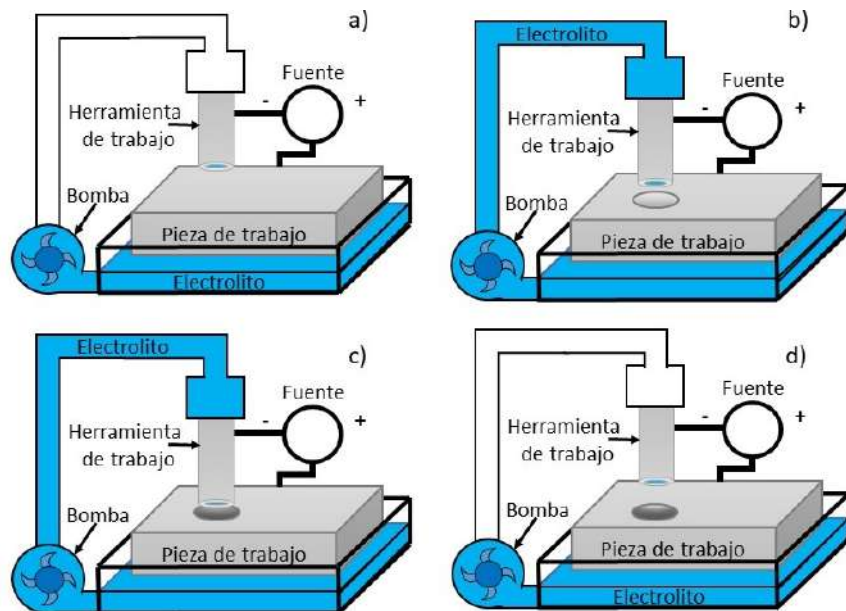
a) Herramienta y pieza de trabajo antes del maquinado. b) Herramienta de trabajo realizando el maquinado sobre la pieza de trabajo. c) Herramienta de trabajo deja de maquinar. d) Pieza de trabajo con material removido después del maquinado.
